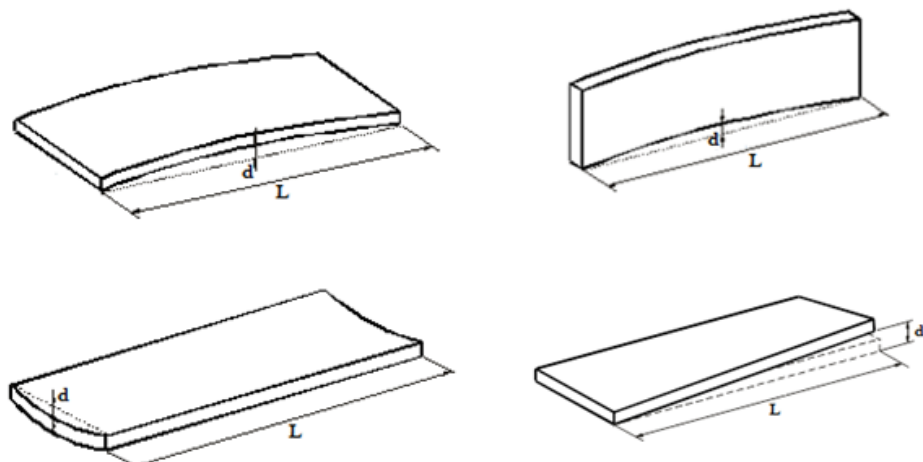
Alabeos de la madera aserrada. (Superior izquierda) Combado. (Superior derecha) Encorvado. (Inferior izquierda) Abarquillado. (Inferior derecha) Revirado.
